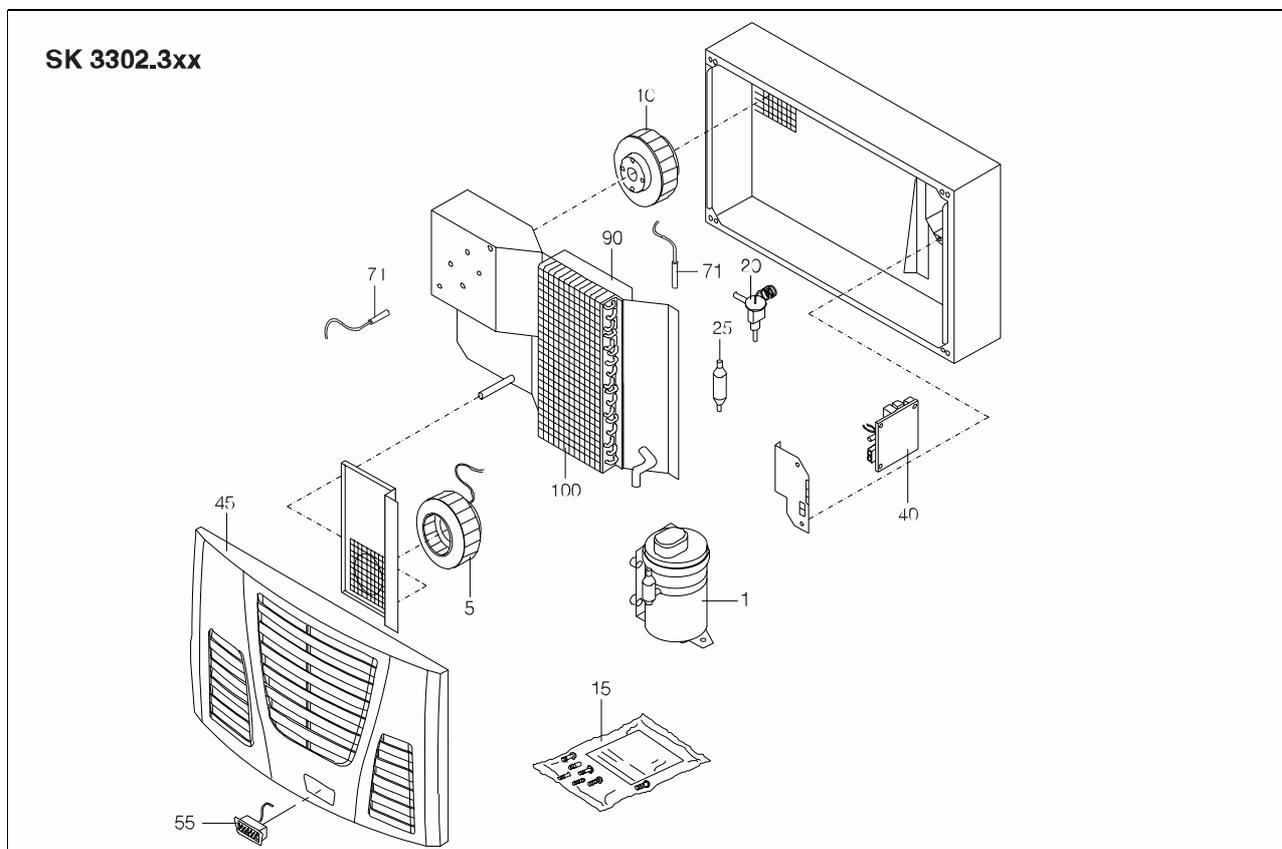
Pièces de rechange pour SK 3302.3xx
